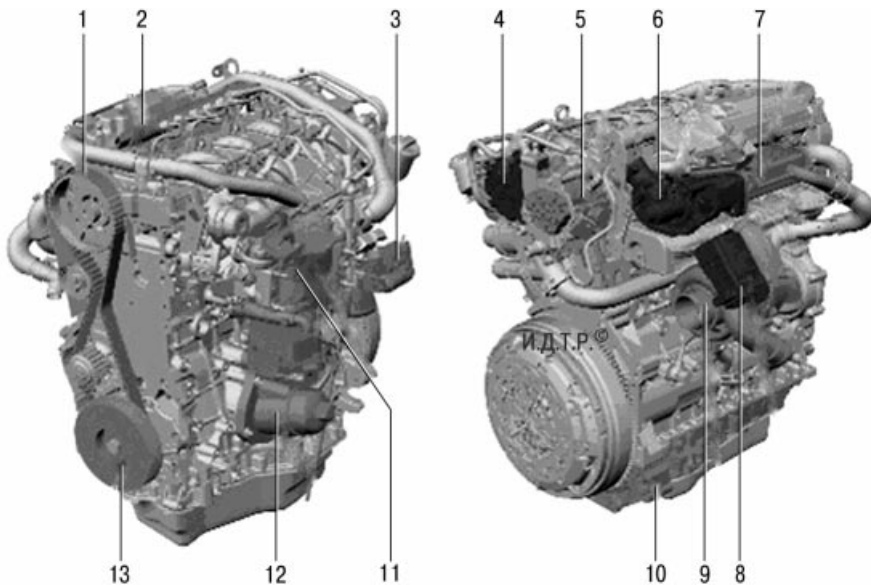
Двигатель Duratorq-TDCi объемом 2,2 л: 1 – ремень привода газораспределительного механизма; 2 – распределительный коллектор системы впрыска топлива; 3 – заслонка впускной трубы с электронным управлением; 4 – вакуумный насос; 5 – топливный насос; 6 – система рециркуляции выхлопных газов (EGR) с электрическим управлением; 7 – радиатор системы EGR; 8 – электрическое исполнительное устройство регулировки направляющих лопаток турбокомпрессора; 9 – турбокомпрессор с регулируемым сопловым аппаратом; 10 – надставка масляного картера; 11 – топливный фильтр; 12 – блок масляный фильтр/масляный радиатор; 13 – демпфер коленчатого вала
